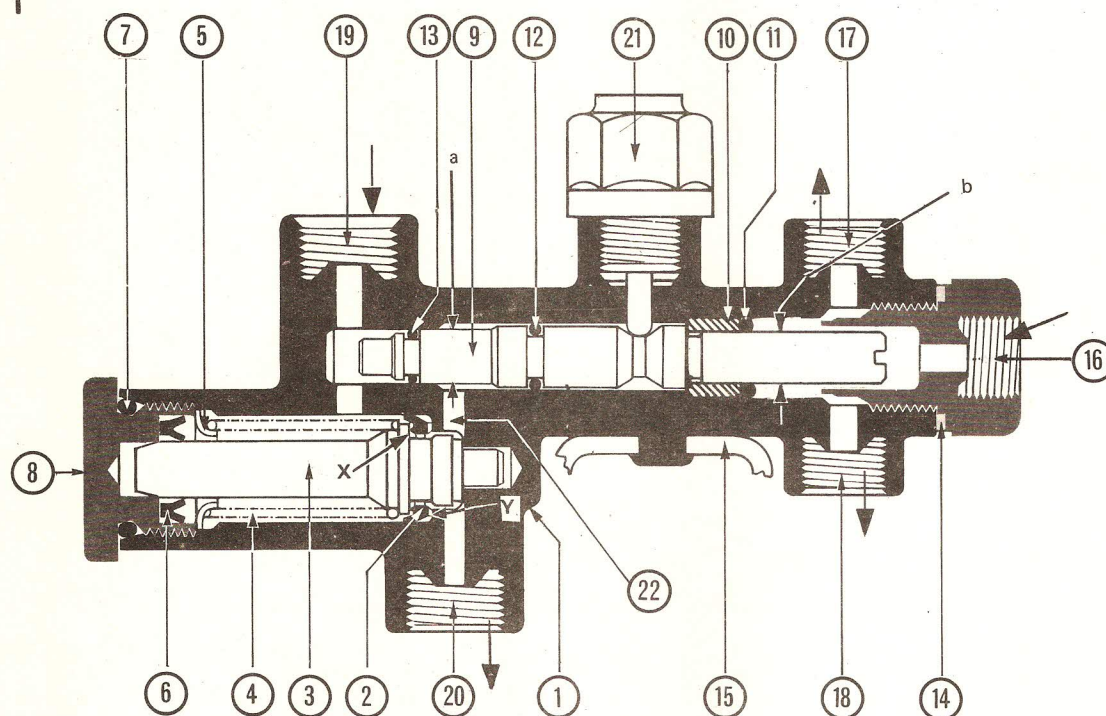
Vista en Corte - Conjunto Válvulas Proporcionadora y Diferencial.
